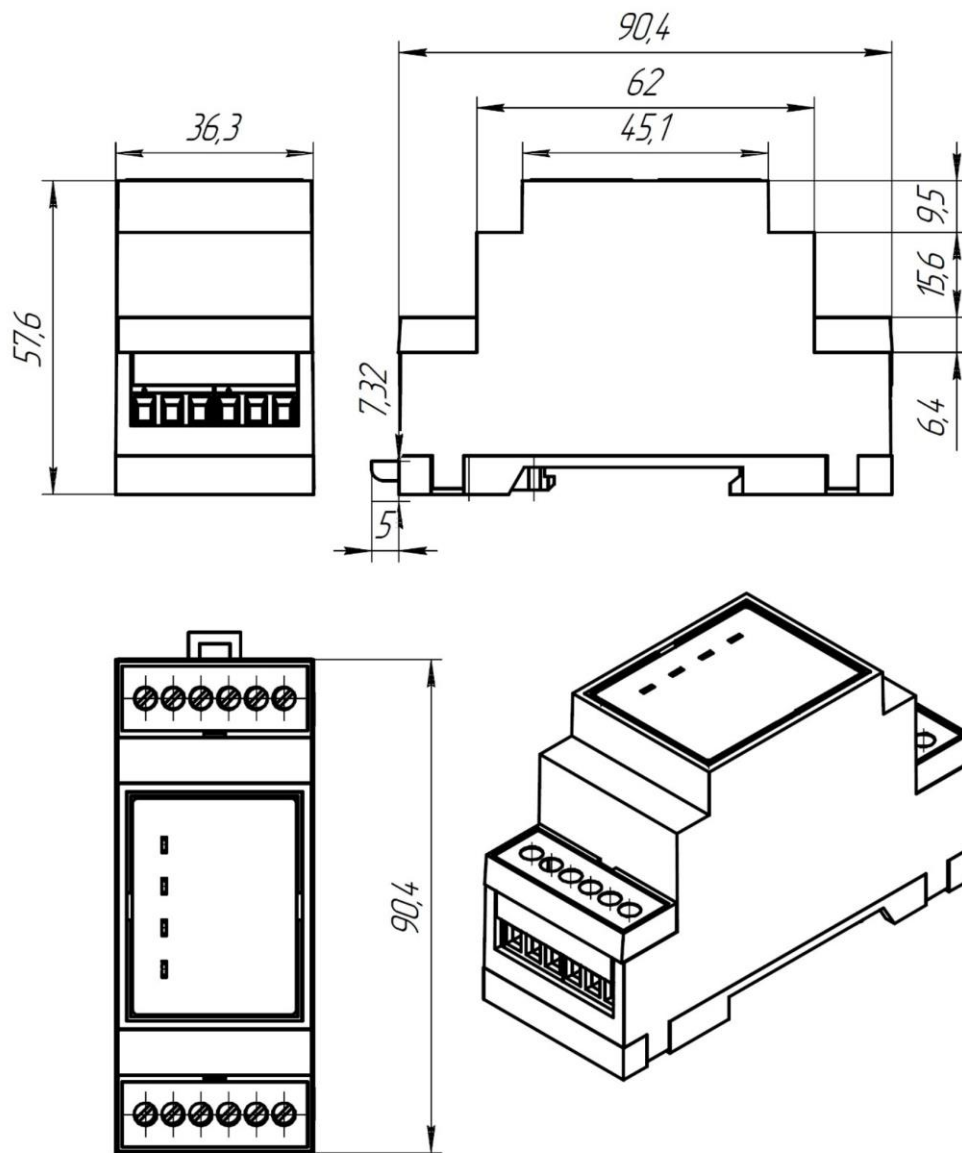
Габаритные размеры повторителя RS484/RS485/RS232 DCE485-01
